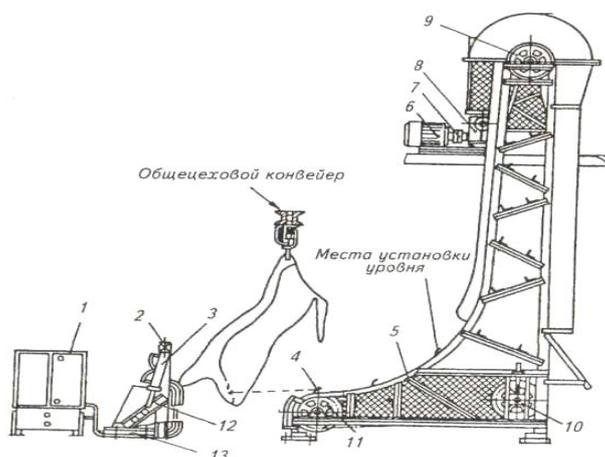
Установка для съемки шкур с туш крупного рогатого скота А1-ФУУ: 1— станция гидропривода фиксатора; 2 - фиксатор; 3- гидроцилиндр; 4 - тяговая цепь; 5- механизм снятия шкуры; 6 - электродвигатель; 7 - муфта; 8 - редуктор; 9 - приводная звездочка; 10 - натяжная звездочка; 11 - поворотная звездочка; 12 - каретка; 13 - рама фиксатора
